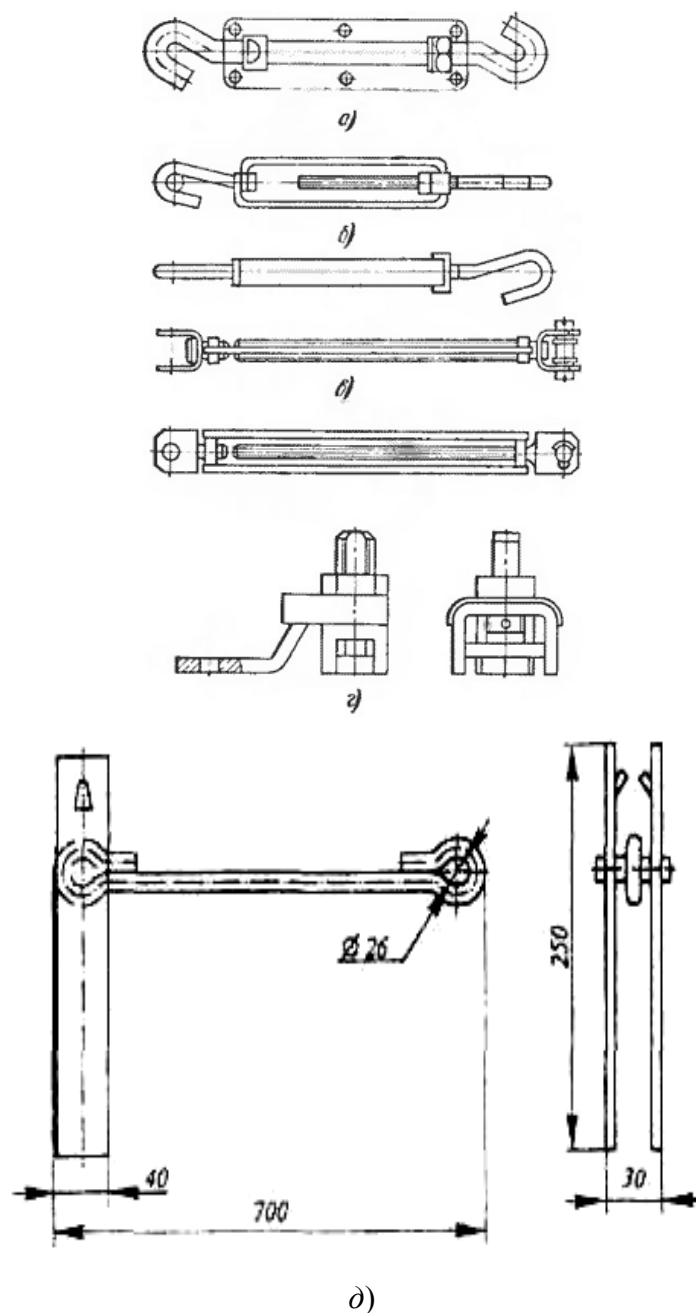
Муфты и приспособления для натяжения тросов и струн:
